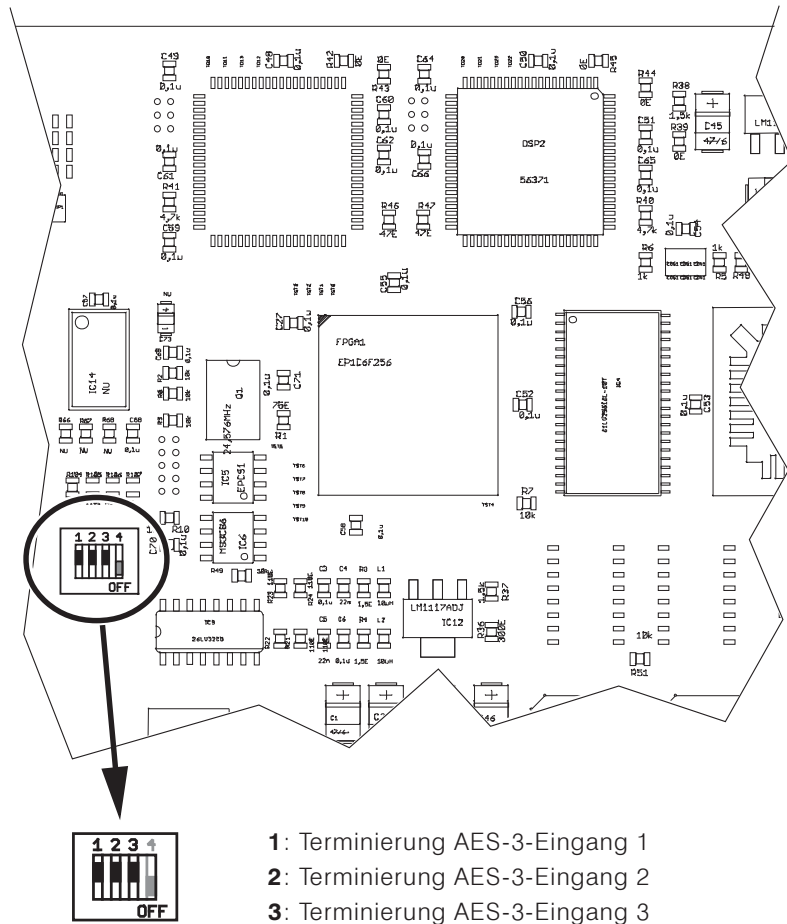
Teilansicht der Hauptplatine mit DIP-Schalter
